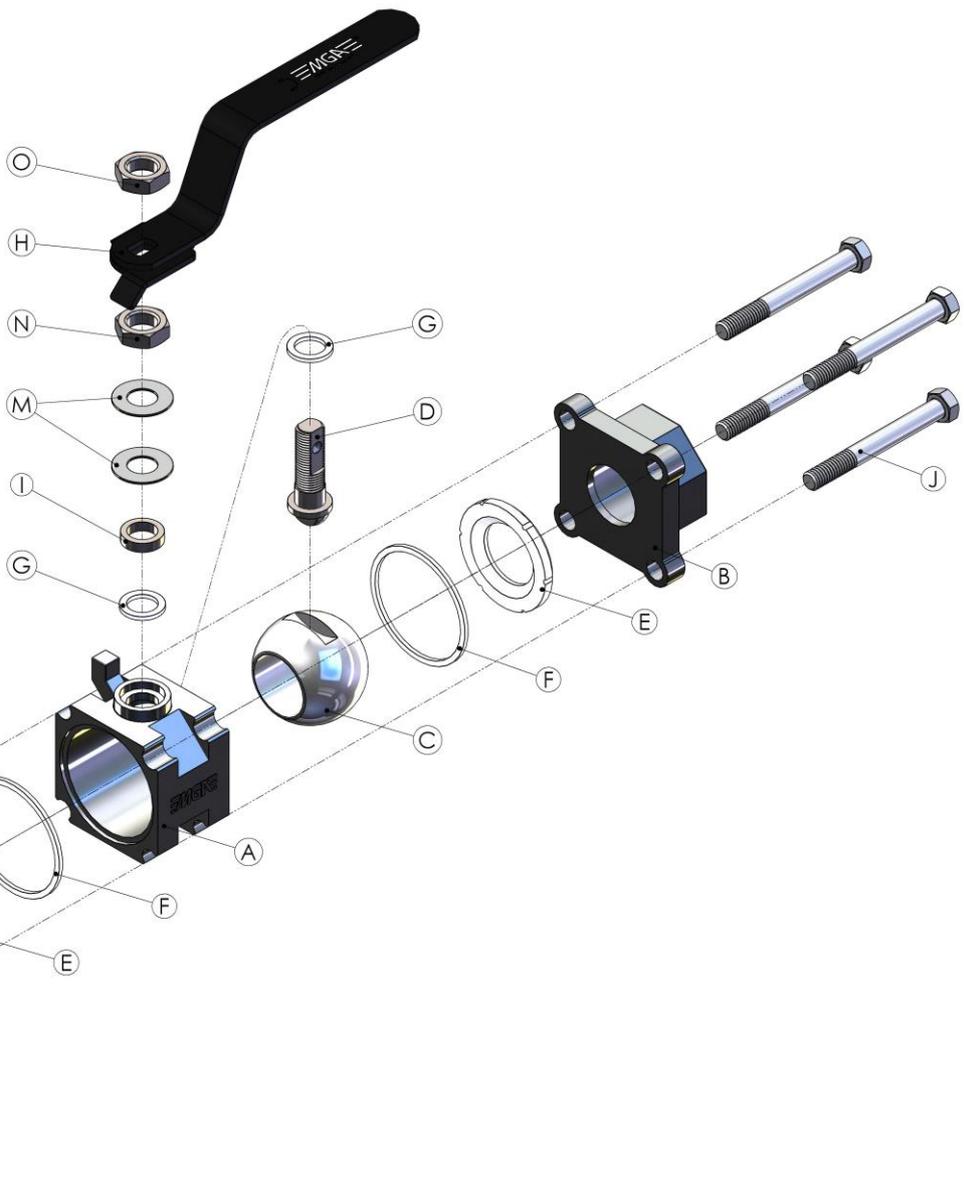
Vista explodida da Válvula de Esfera CL300 (Sequência de montagem)
